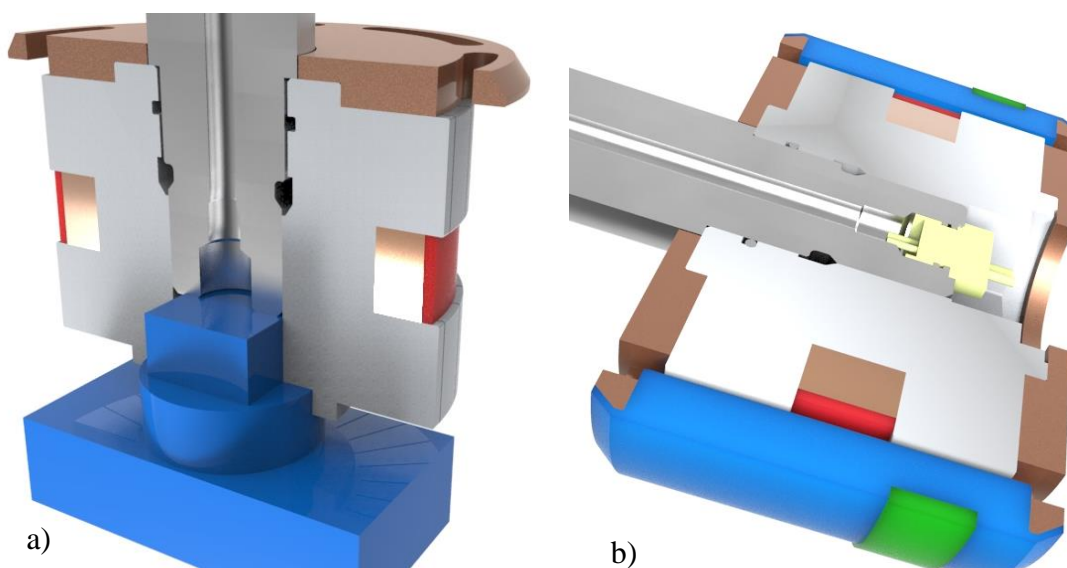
51 Utahování pístnice a jádra MR tlumiče; detail přípravku pro utáhnutí
